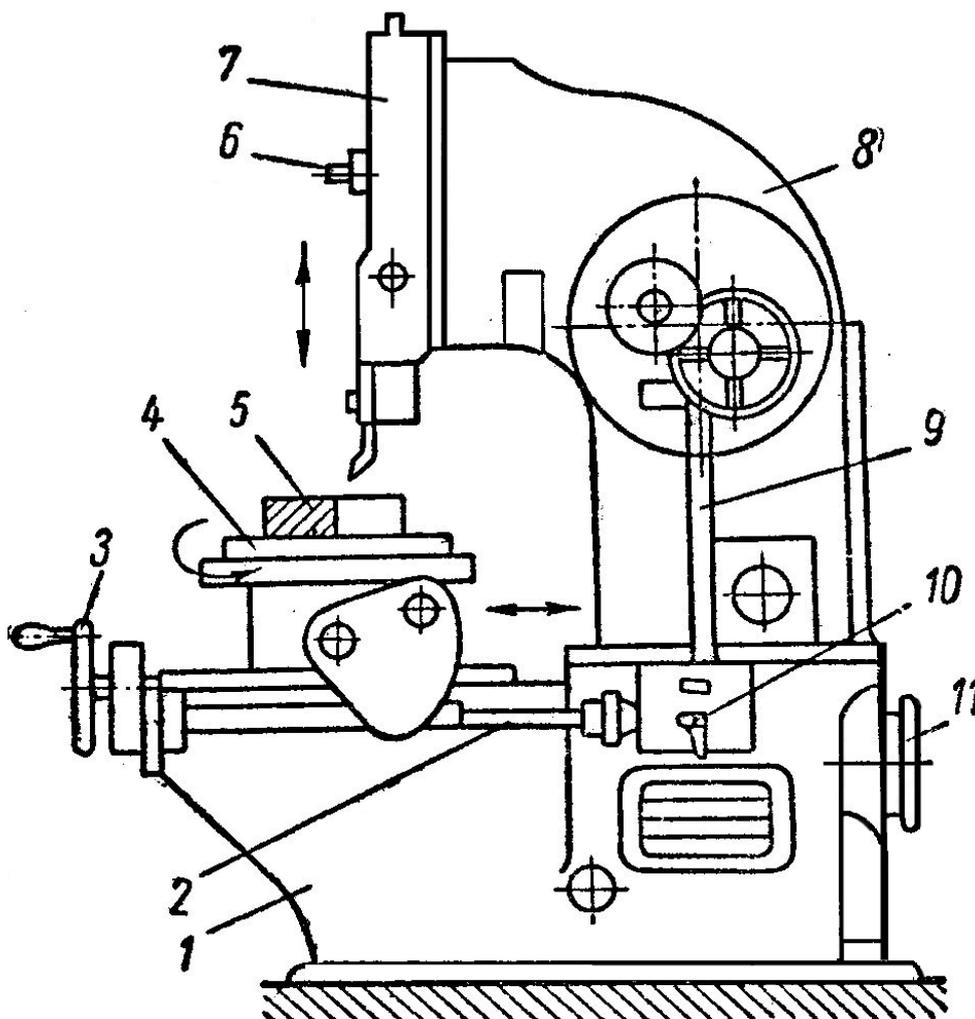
Общий вид долбежного станка: 1 – станина; 2 – винт; 3 – маховик; 4 – стол; 5 – заготовка; 6 – зажим; 7 – долбежная головка; 8 – корпус; 9 – колонна; 10 – рукоят-
